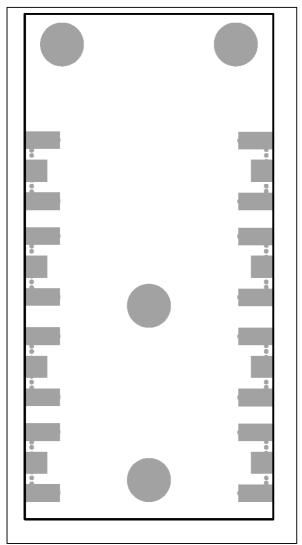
MAX3787 评估板 PC 板布局——焊接层
